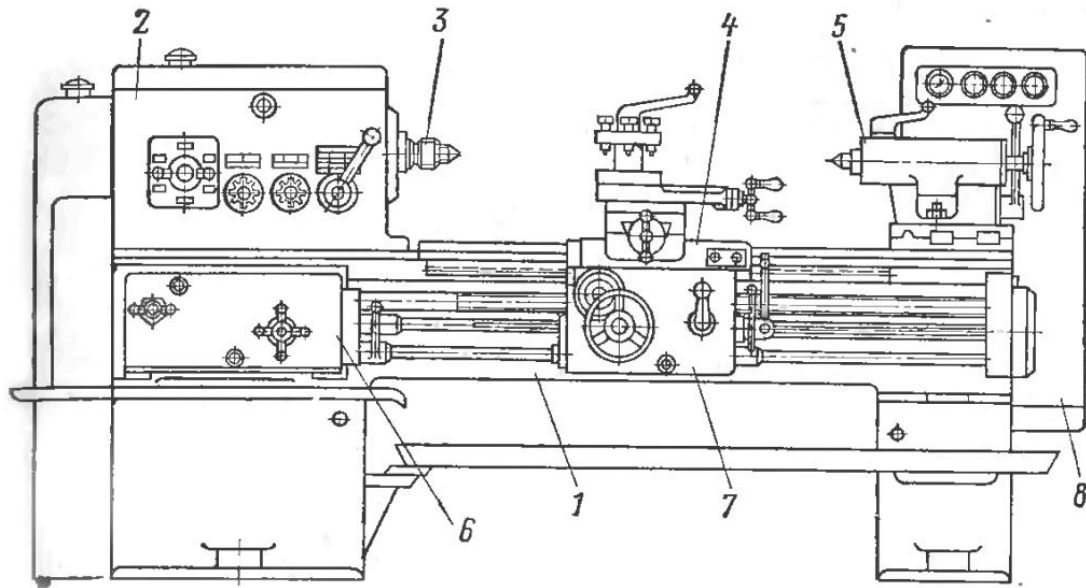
Загальний вигляд токарно-гвинторізного верстата моделі 1К62Б
